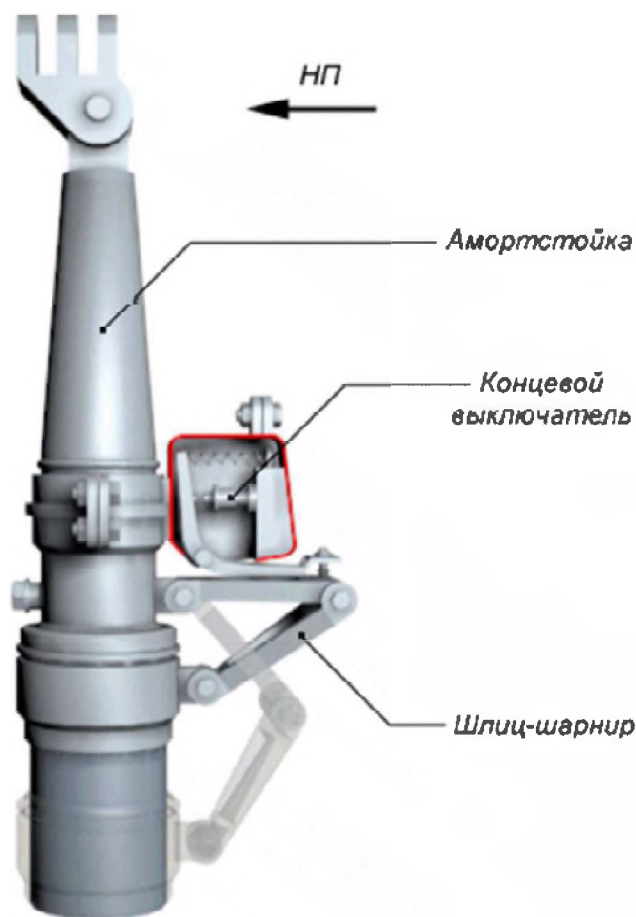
Расположение шлиц-шарнира и концевого выключателя главной стойки Ми-8 [10]
